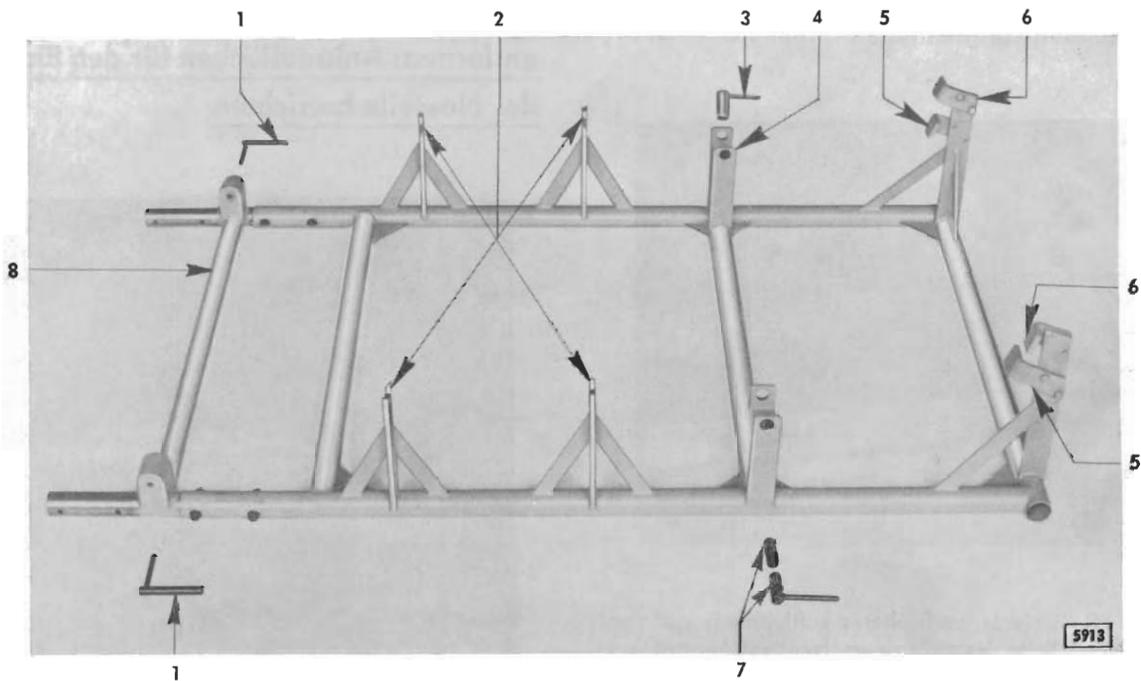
Längsträger-Hinterteil-Schweißlehre S-1286
